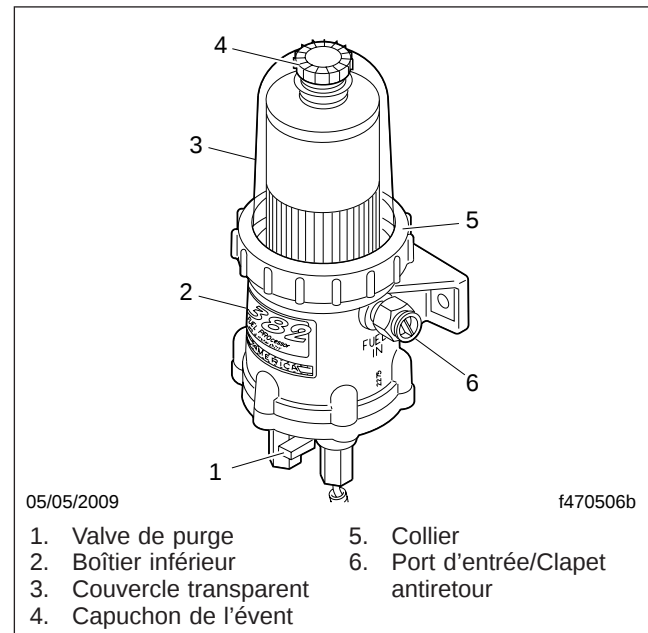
, Séparateur carburant/eau DAVCO (modèle Fuel Pro 382 illustré)
